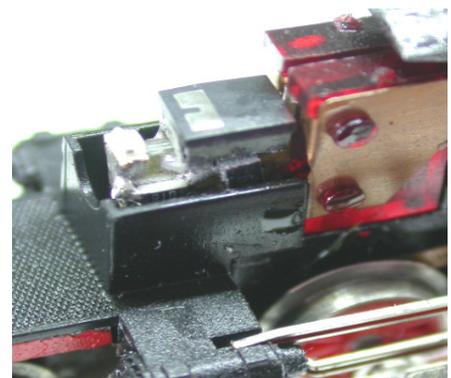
Korrekter Sitz, Baustein ganz eingeschoben
